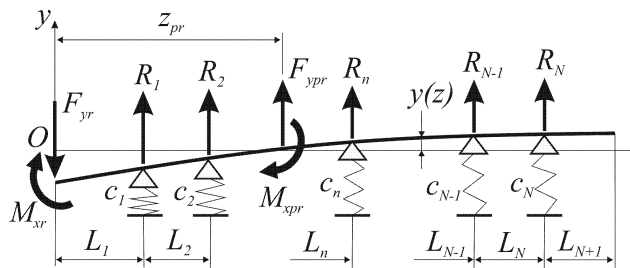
Розрахункова схема N опорного шпindelного вузла.
